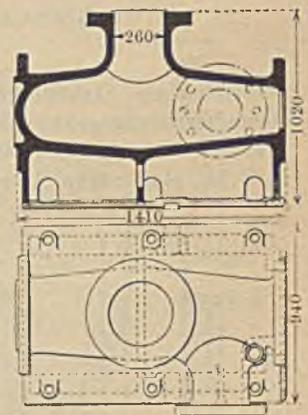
Einseitig geschlossener Pumpenkörper. Gewicht 2325 kg. (Gutehoffnungshütte.)
